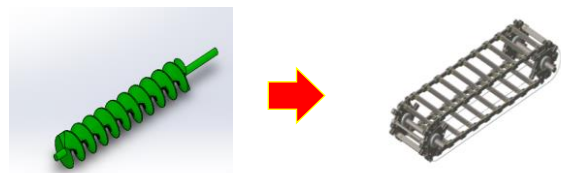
การออกแบบเครื่องจักรส่วนที่ 1 เพื่อแก้ไขปัญหาหินติด Screw Conveyor 2 Coal ก้อนใหญ่ติด Screw Conveyor
